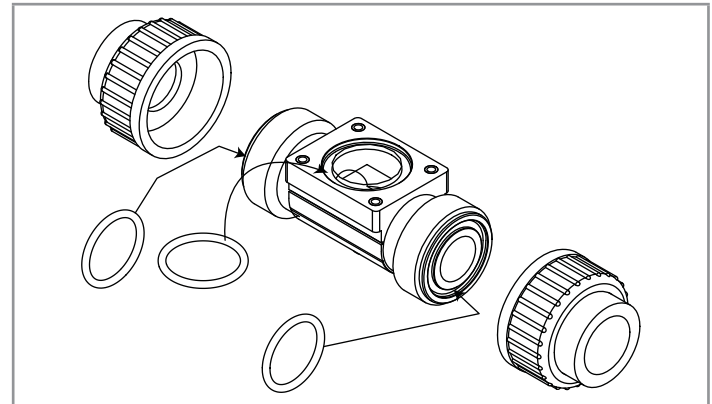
O-Ring-Dichtungen für Kunststoff-Fitting
